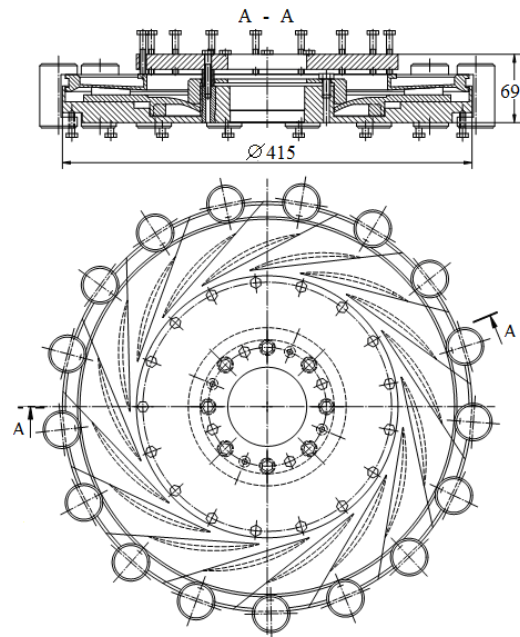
Конструкция сборочно-сварочной оснастки, предназначенной для ЭЛС элементов диффузора прорезными швами
